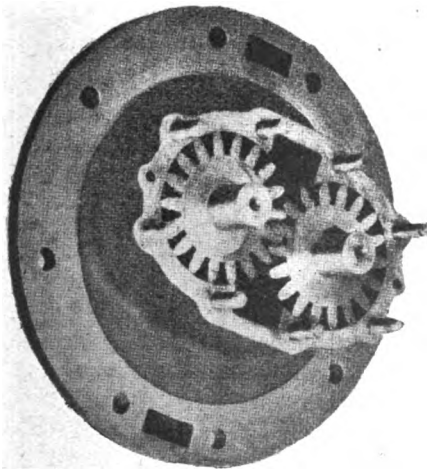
Pompe à engrenages destinée aux petits régulateurs.
